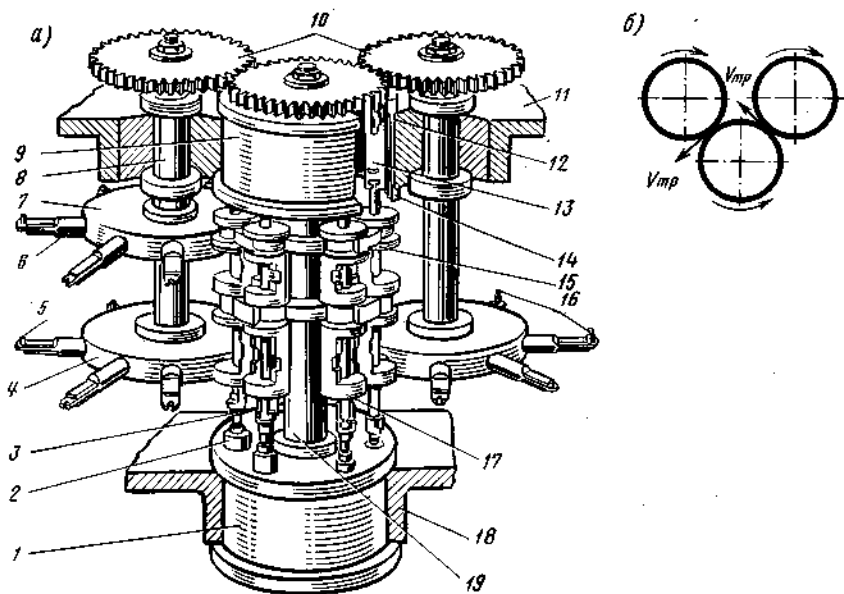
Типовая роторная линия для сборки двух деталей:
